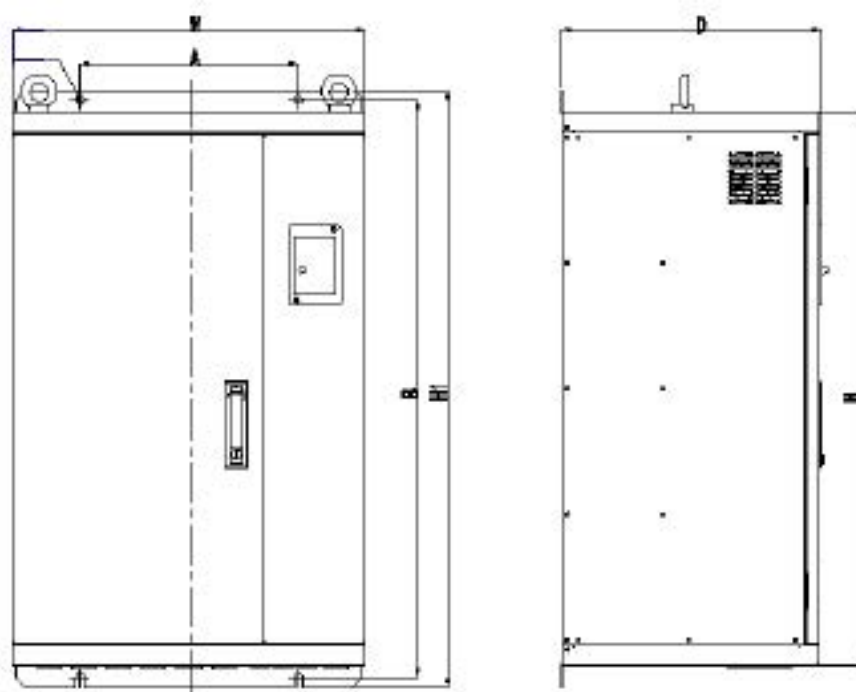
AD1000 系列钣金结构外型尺寸及安装尺寸示意图
